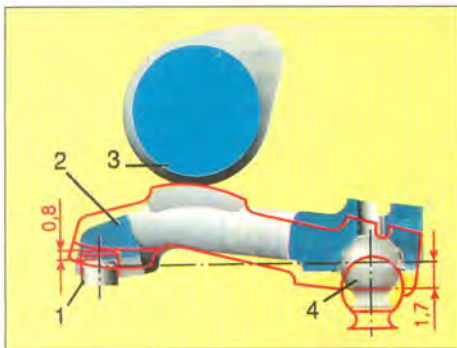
“Жигулевский” механизм привода клапана, красным показано предлагаемое изменение геометрии. 1 – стержень клапана; 2 – рычаг привода; 3 – распределитель; 4 – регулировочный болт.
